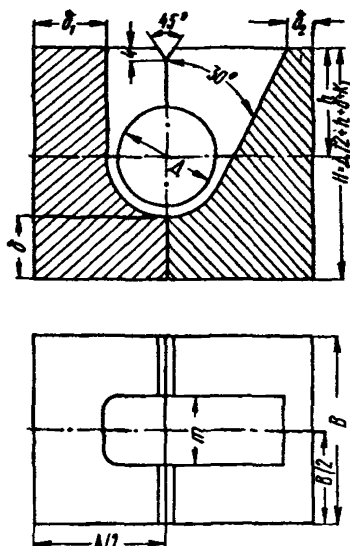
Конструкция медных форм для дуговой многоэлектродной ванны сварки труднодоступных соединений однорядных горизонтальных стержней
